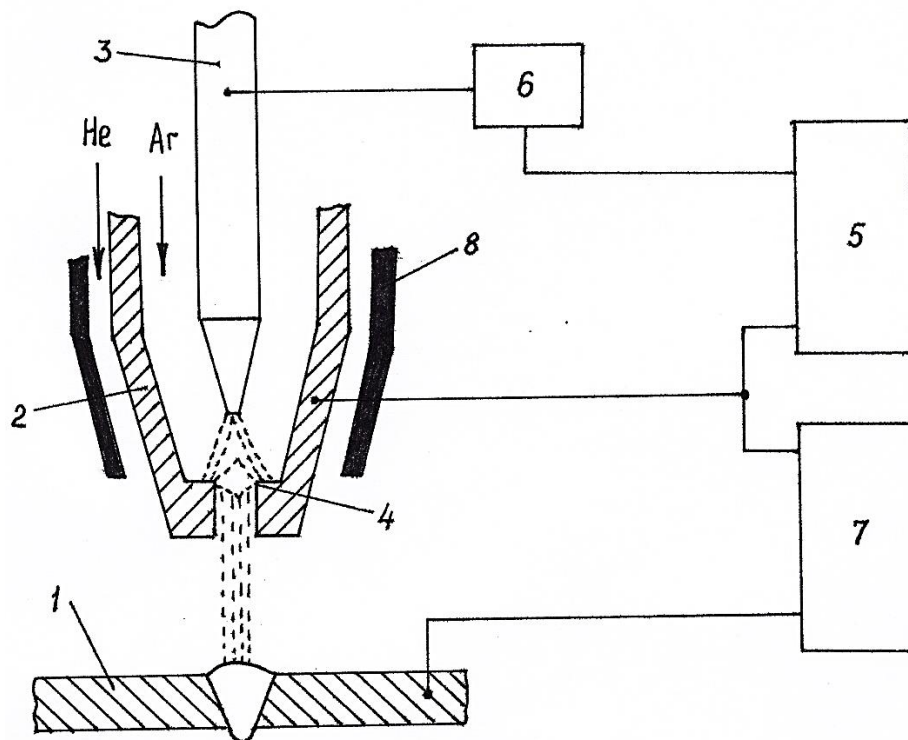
Схема подключения плазмотрона при сварке с полым анодом: 1 – образец; 2 – плазмообразующее сопло; 3 – вольфрамовый электрода; 4 – дежурная дуга; 5, 7 – источники питания дуги постоянного тока; 6 – высоковольтный осциллятор; 8 – газозащитное сопло
